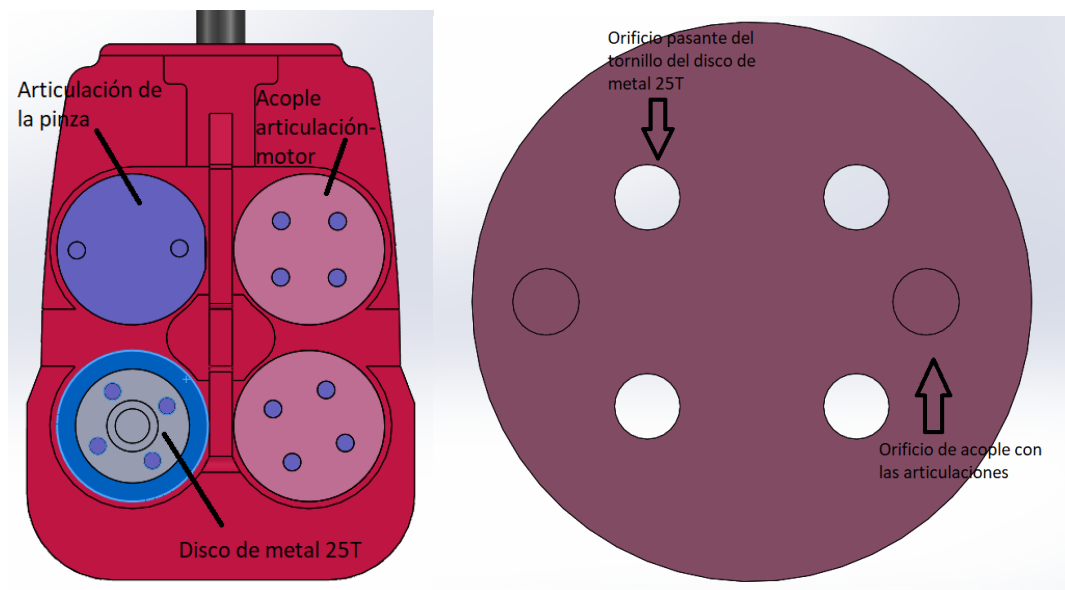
Pieza 3D "Acople articulación/motor" diseñado en SolidWorks
